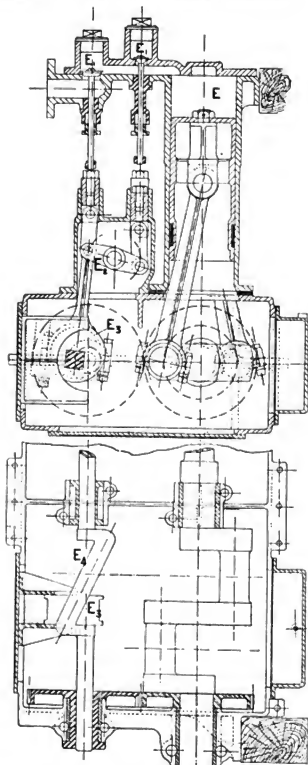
u. 5. Längsschnitt durch Cylinder und Steuerung, und Grundriss der Kurbelordnung.
